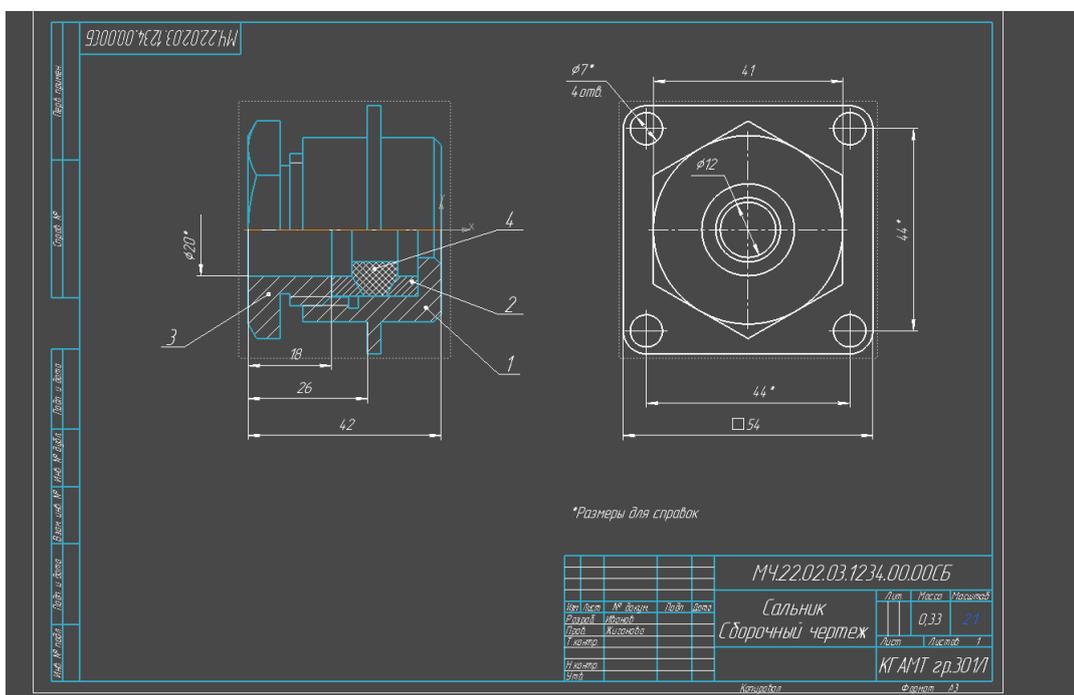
б – Оформление сборочного чертежа Сальника на основе модели
